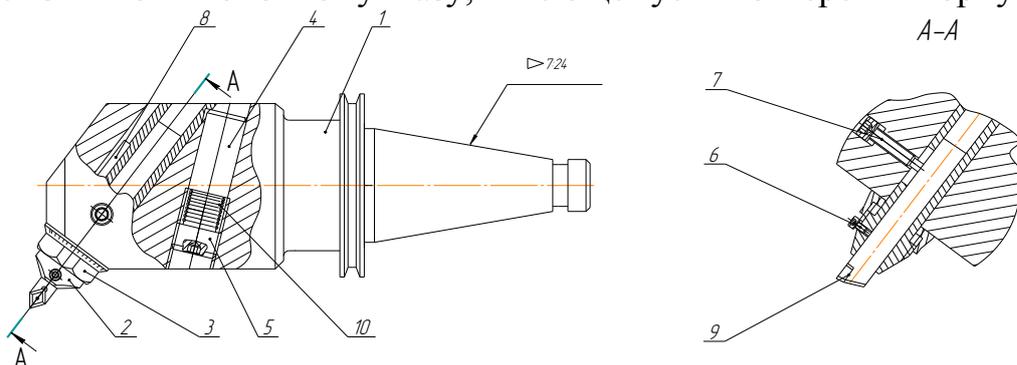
Расточная оправка с микрометрической регулировкой вылета державочного резца
